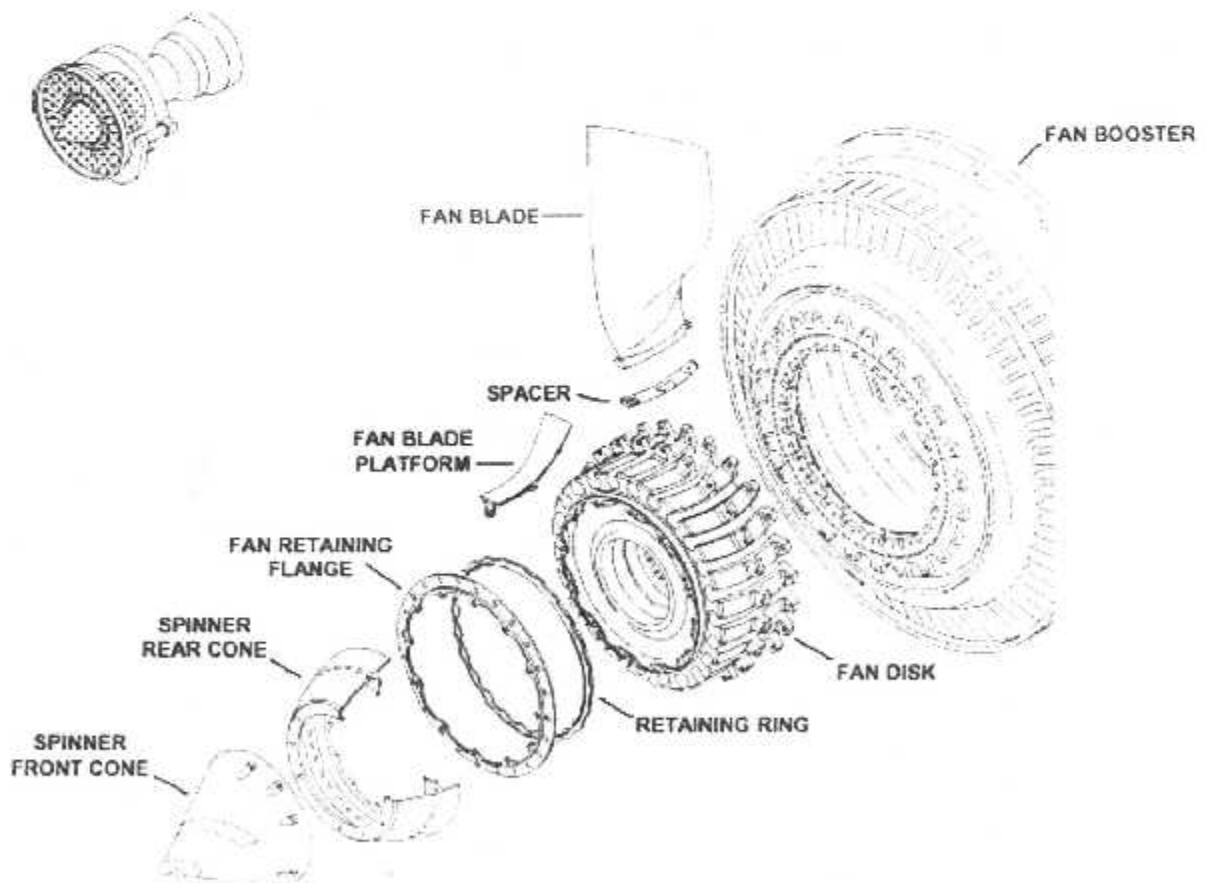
L'ENSEMBLE AILETTES FAN ET CONE
